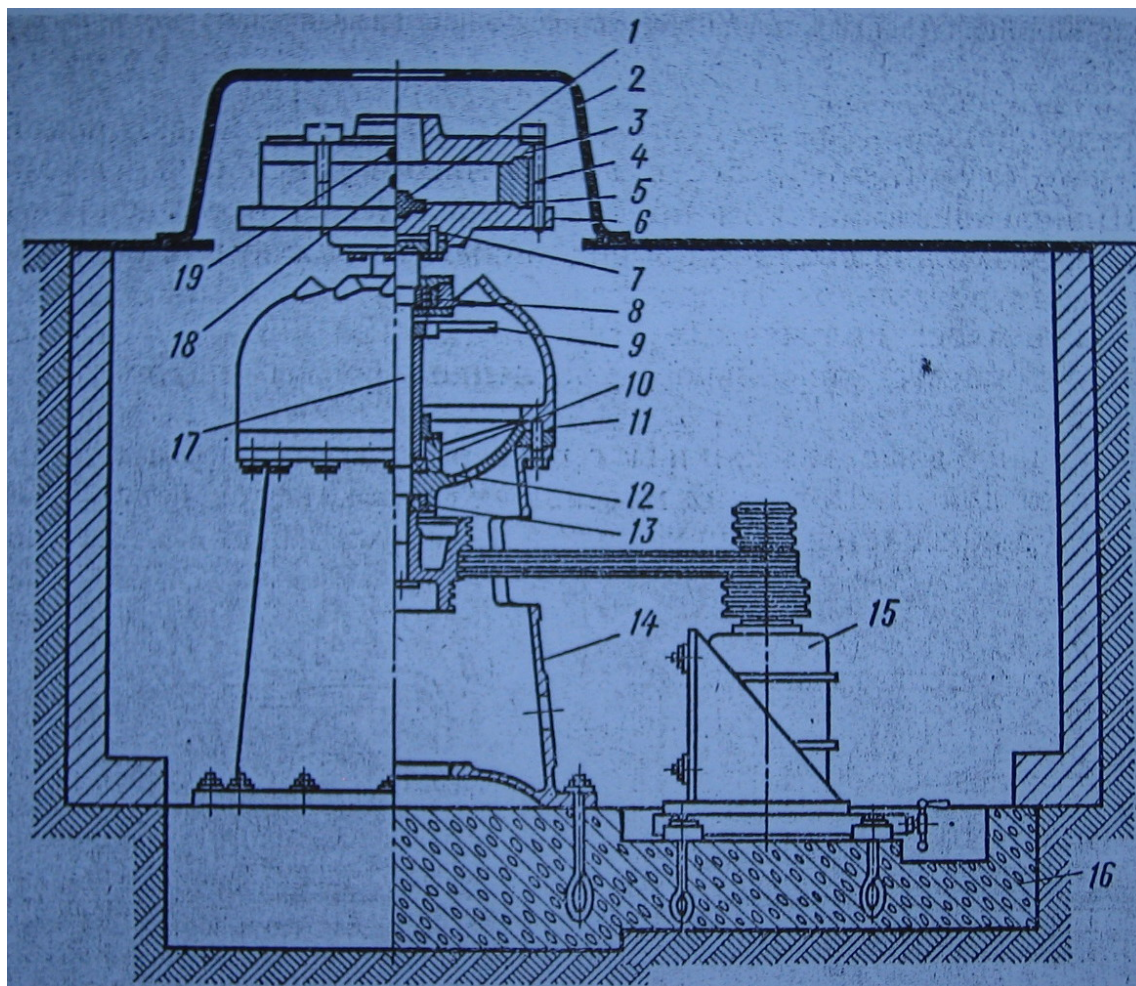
Машина с вертикальной осью вращения. 1- рассекатель, 2- защитный кожух, 3- крышка, 4- болты, 5- корпус формы, 6- поддон, 7- прокладка, 8, 12, 13- подшипники, 9- вентилятор, 10- опорное кольцо, 11, 14- корпус машины, 15- электродвигатель, 16- бетонное основание, 17- шпindelь, 18, 19- цапфы.
